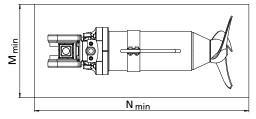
Установка принадлежностей 22 - Amamix 200/300/400 (кроме типоразмера 4135)
